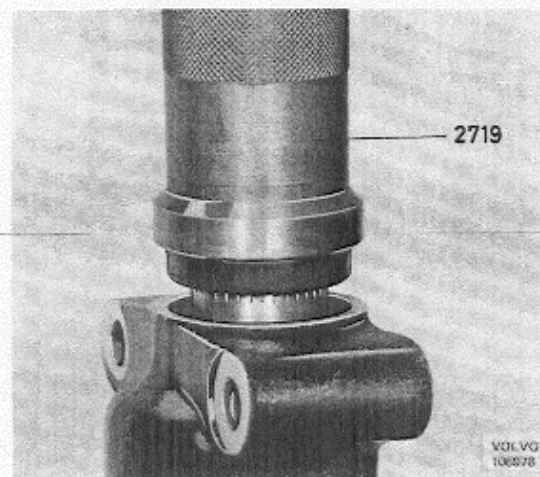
Einpressen des Dichtrings, Lenkrollenwelle
